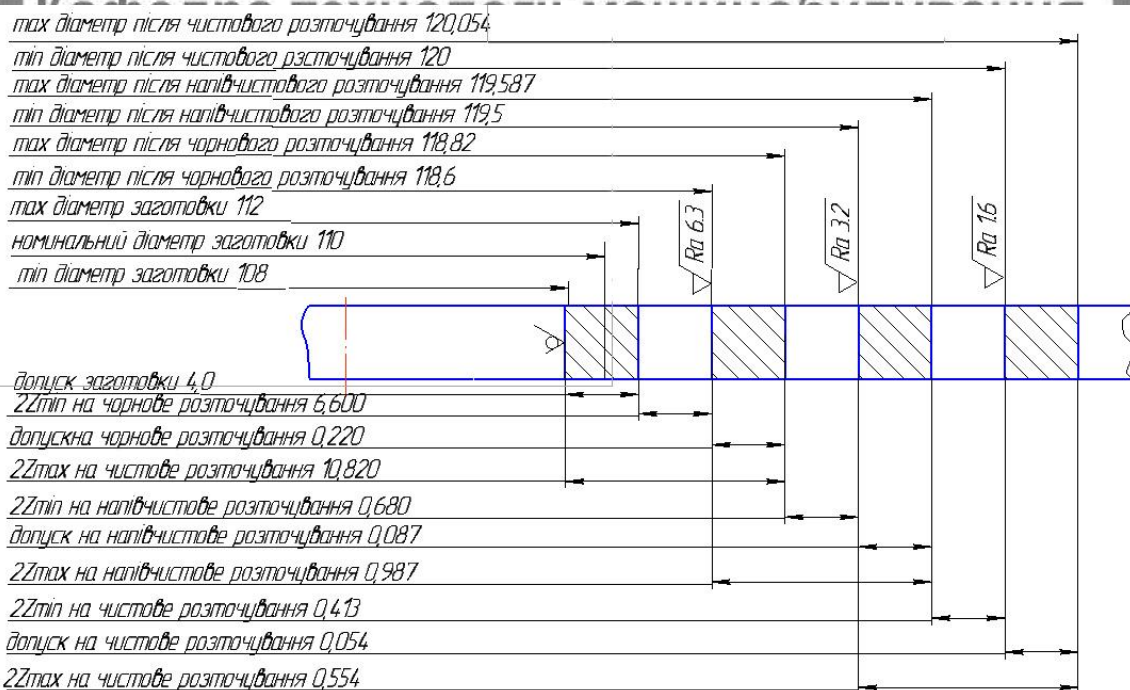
Схема розміщення допусків з припусками при обробці діаметрального розміру  $\varnothing 120H8^{(+0.054)}$  плунжера
